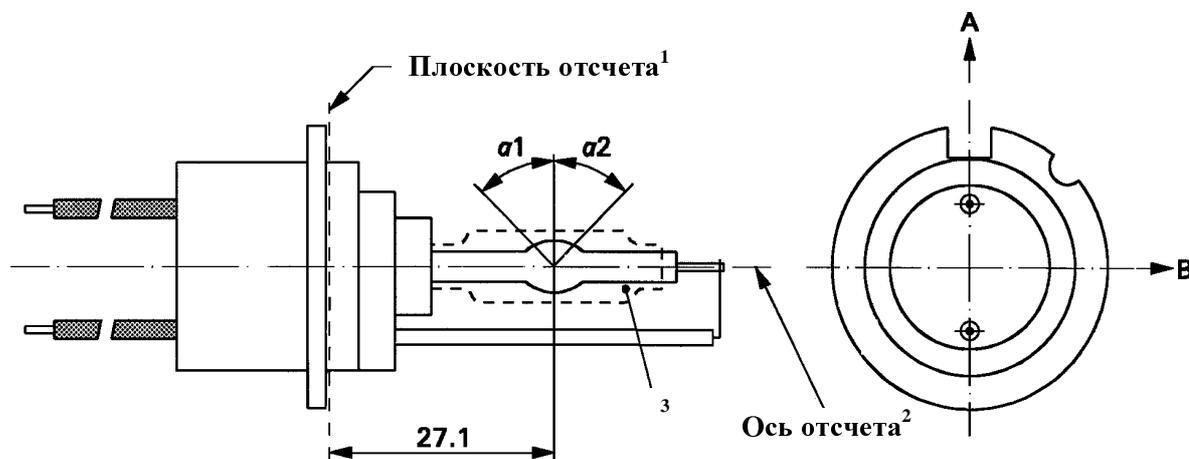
Категория D3S - Типовой газоразрядный источник света с пусковым приспособлением -
